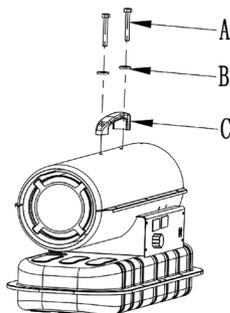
Внешний вид Hintek DIS 10, DIS 20
